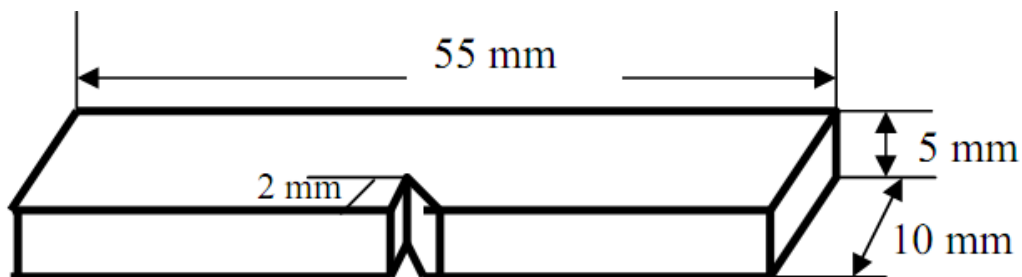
Forme et dimensions de l’éprouvette de résilience.
